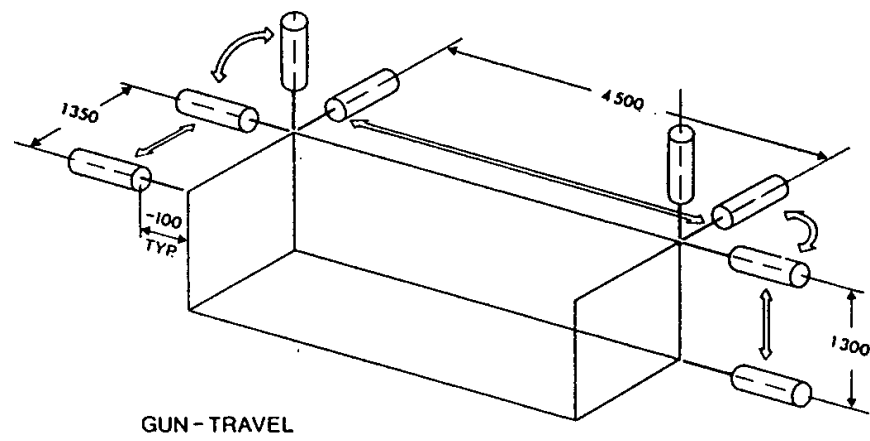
MBB; impianto per saldatura Electron Beam.
